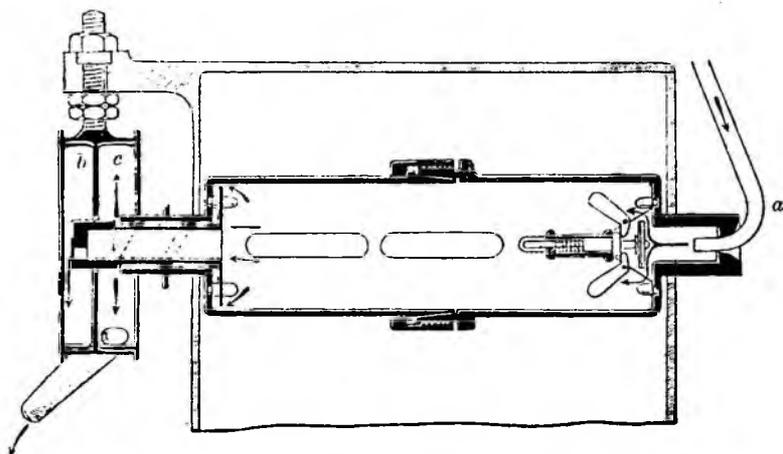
Ручная центрофуга Арнольдта, модель SX; вертикальный разрез через цилиндр: а—трубка, подводящая молоко; б—камера для сливок; с—камера для обезжиренного молока.
